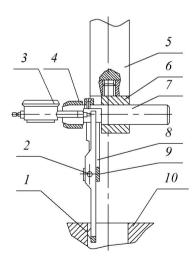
Приспособление для центрирования: 1 – упор; 2 – ось стойки; 3 – индикаторная головка; 4 – гайка; 5 – шпиндель; 6 – колодка; 7 – державка; 8 – рычаг; 9 – ограничитель; 10 – гильза
